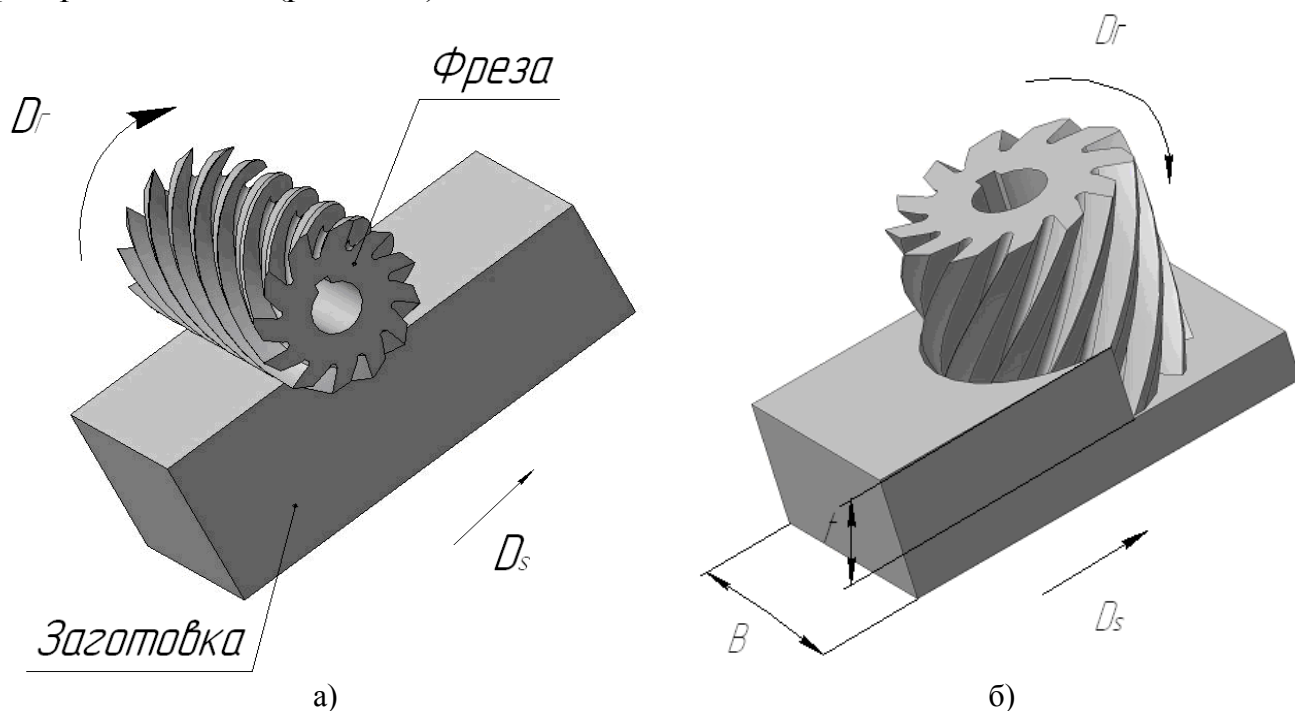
Схема обработки при цилиндрическом (а) и торцовом (б) фрезеровании
